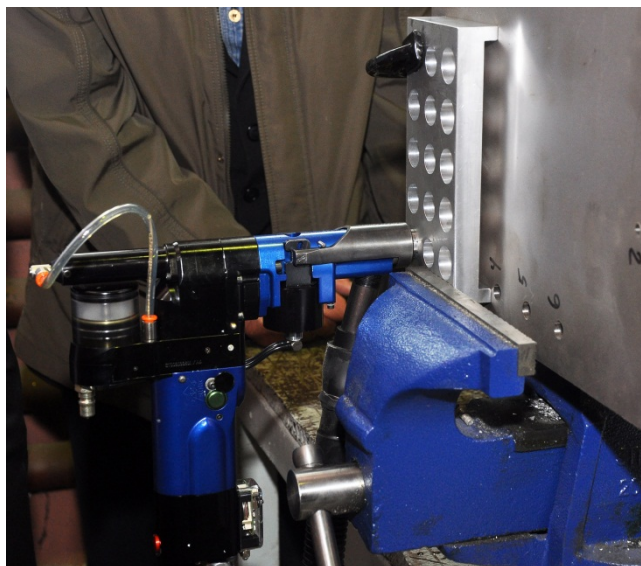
Фиксация СМАП на обрабатываемой поверхности с помощью кондуктора
